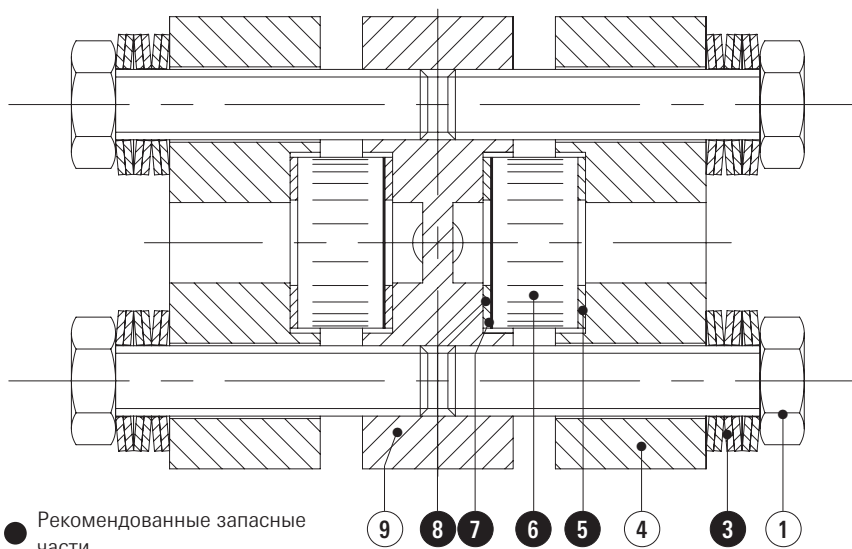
Указатель уровня с прозрачным стеклом, Тип: 'MT' Конструкция с использованием резьбовой шпильки и гайки
